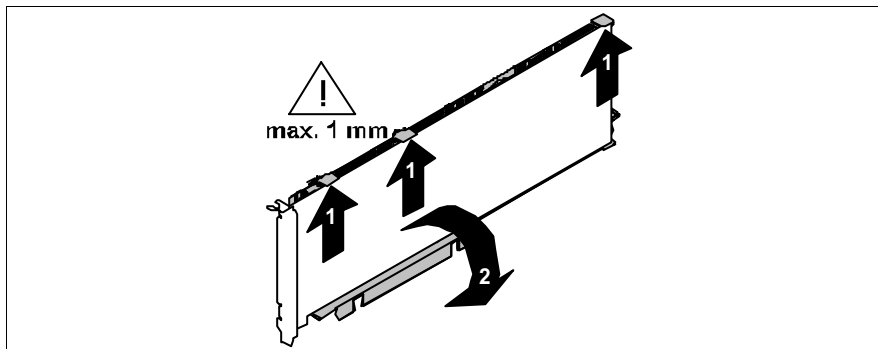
Retirer une carte PCI "hot-plug" du dispositif de fixation
